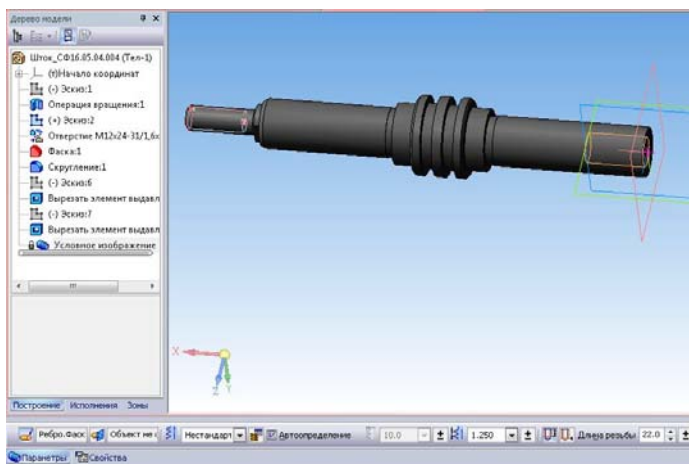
Побудова різьблення на поверхні деталі Шток
